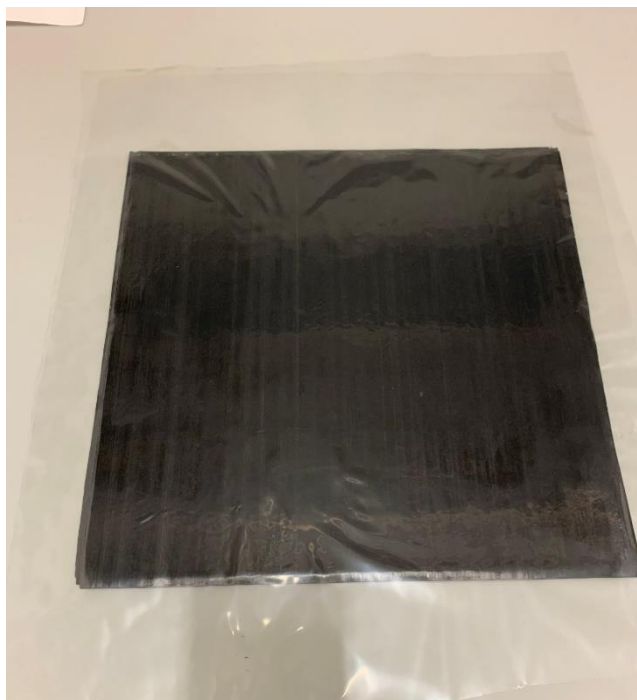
Placa de carbono-epóxico com filme de desmoldante
